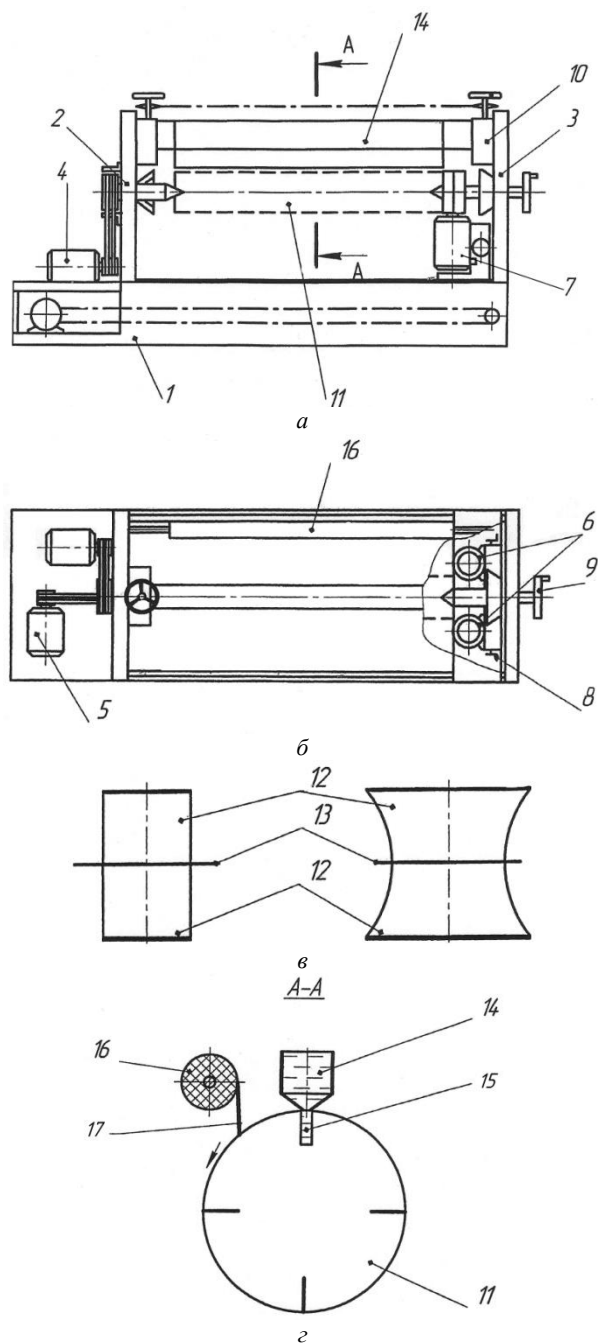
Схема станка для обработки бревен: *а* – вид спереди; *б* – вид сверху; *в* – сборные фрезы (слева – с плоскими ножами, справа – с профильными); *з* – узел для нанесения клея и упаковки в пленку
